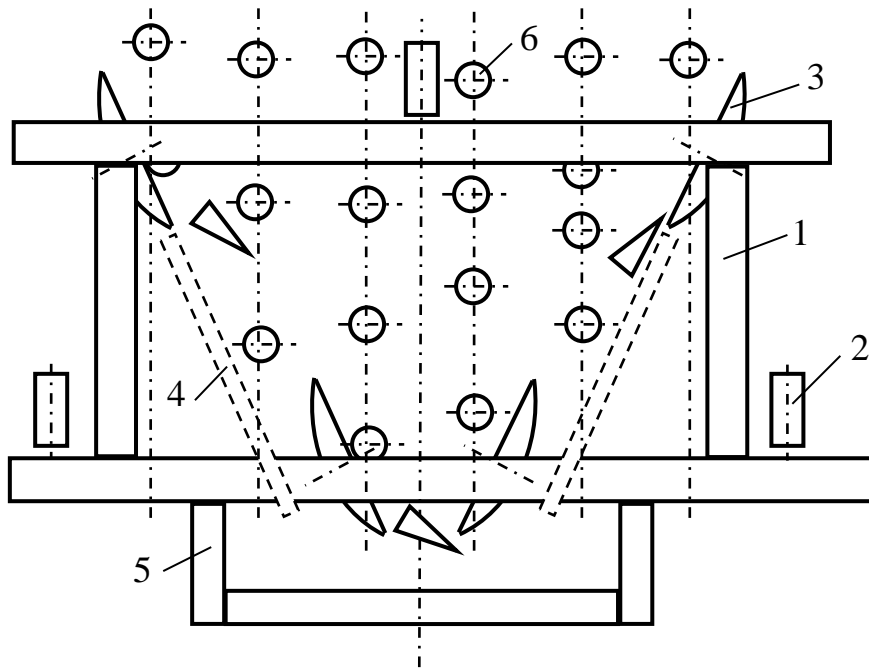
Конструктивна схема польової установки для викопування кормових буряків: 1 – рама; 2 – опорні регульовальні колеса; 3 – сферичний диск; 4 – полоз з ножом; 5 – сниця; 6 – коренеплід
